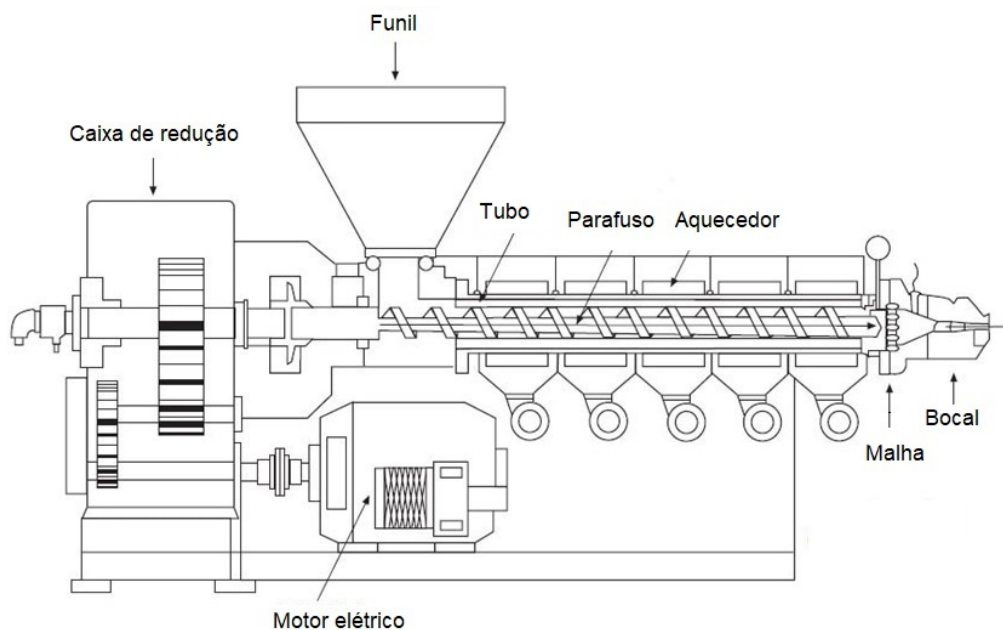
Máquina extrusora e componentes, adaptada de Giles et al. [1].
